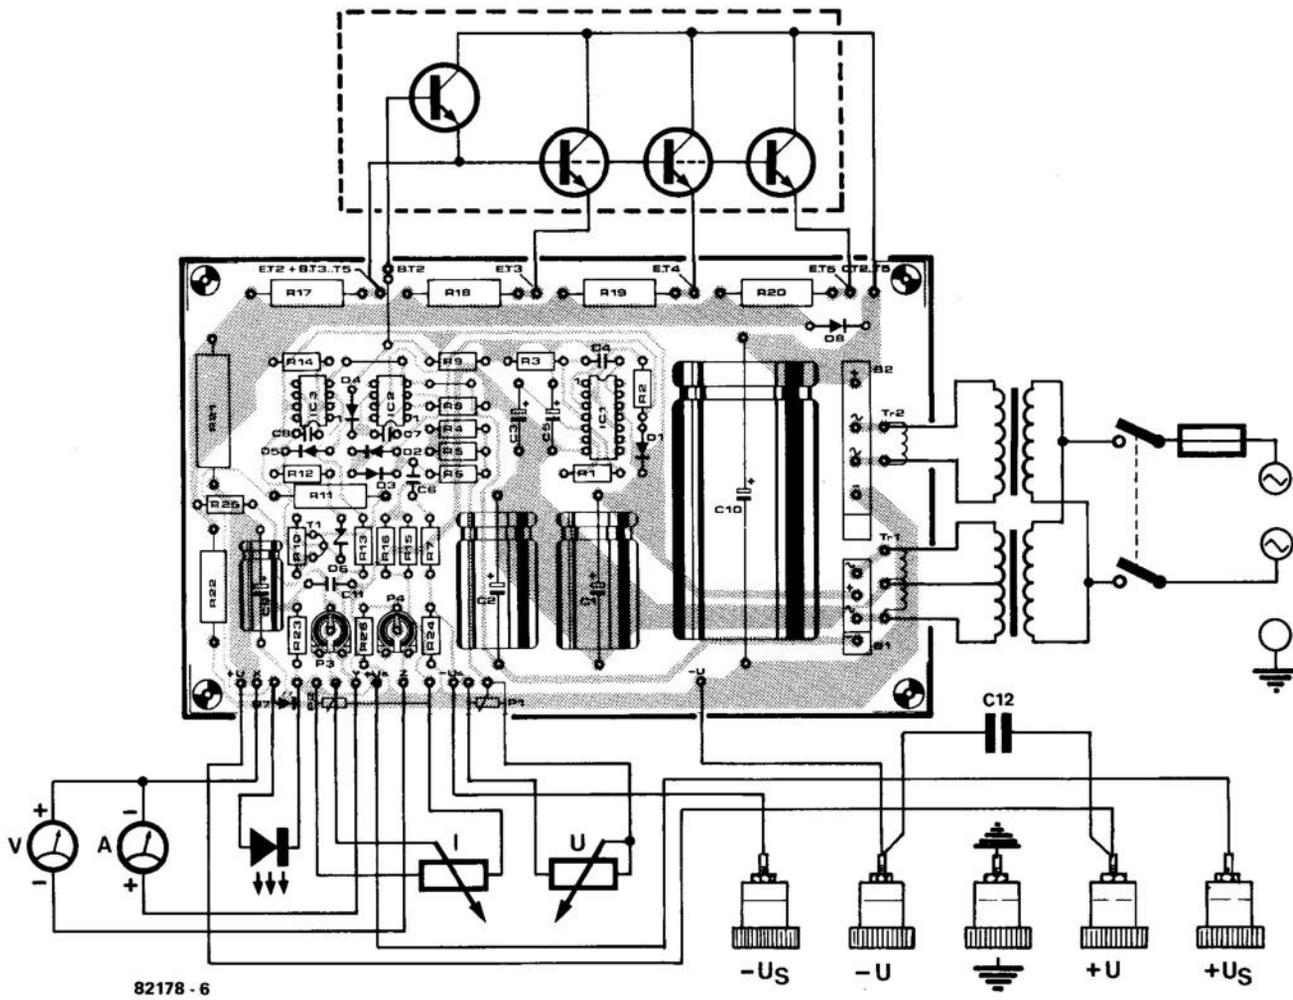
Mit Verdrahtungsplan geht alles leichter.
